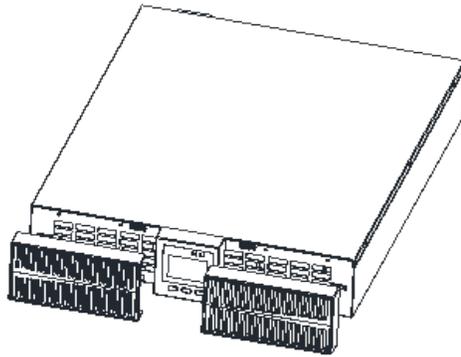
EXTRACCIÓN DE CUBIERTA DE PLÁSTICO FRONTAL
